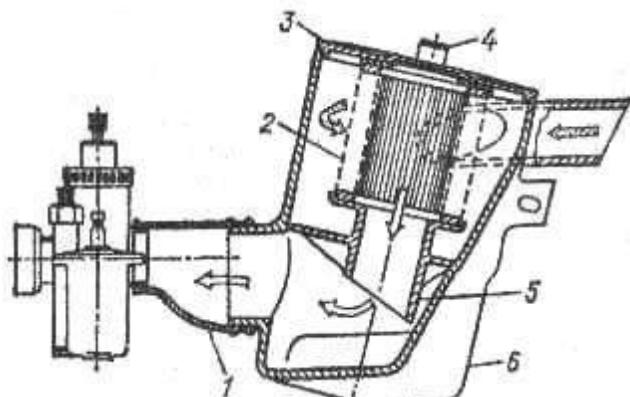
Разрез глушителя шума впуска с воздухофильтром мотоцикла "Ява-250" и схема его работы (стрелками показано направление движения воздуха):
